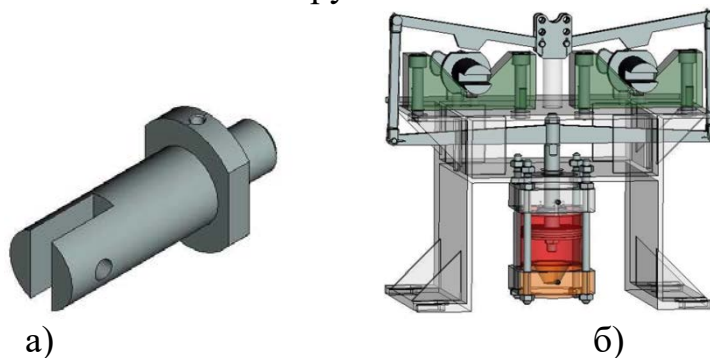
а) - деталь (тяги), б) - верстатний пристрій 3D
